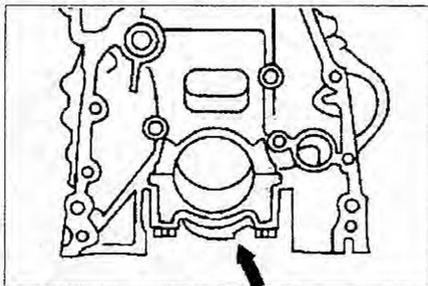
Проверка правильности установки крышек коренных подшипников.
